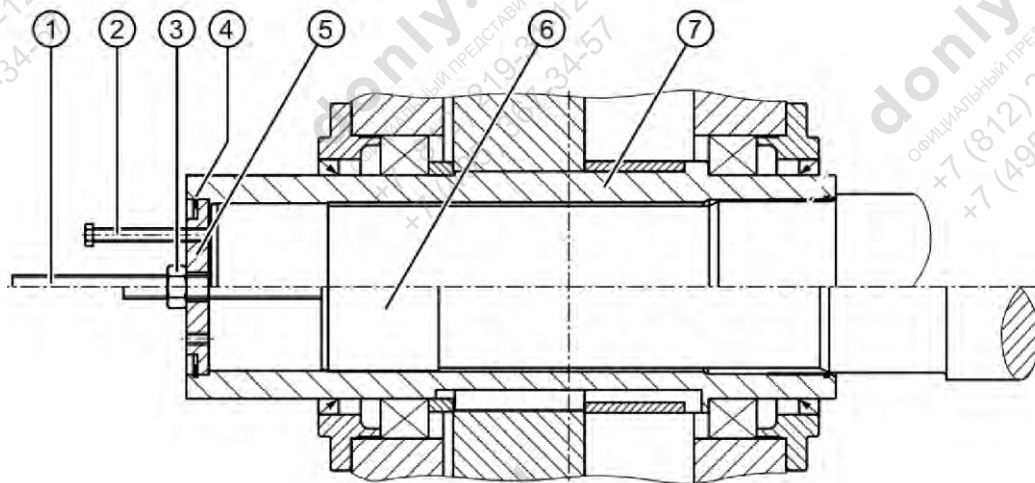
Подготовка редукторов с полым валом и усадочным диском
